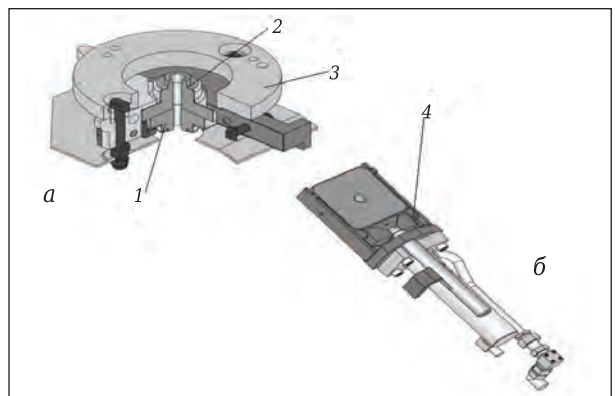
Компоновка оборудования разливочного отверстия (а) и манипулятора (б) для замены нижнего стакана-дозатора: 1 — нижний стакан; 2 — верхний стакан; 3 — корпус; 4 — манипулятор для замены нижнего стакана-дозатора
